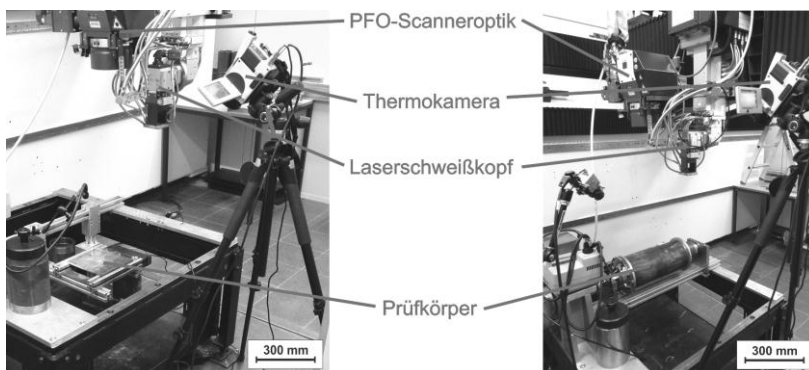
Versuchsaufbau für die Laserstrahlschweißungen an linearen Schweißnähten (links) und an den radialen Rundnähten an Rohren (rechts)
